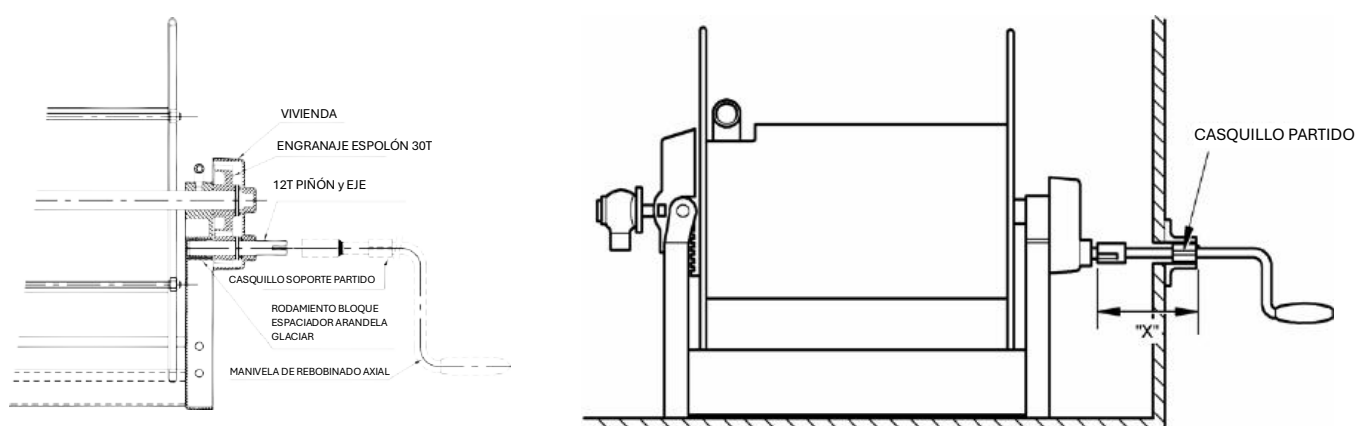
Enrollador de mangueras con rebobinado axial por engranajes
